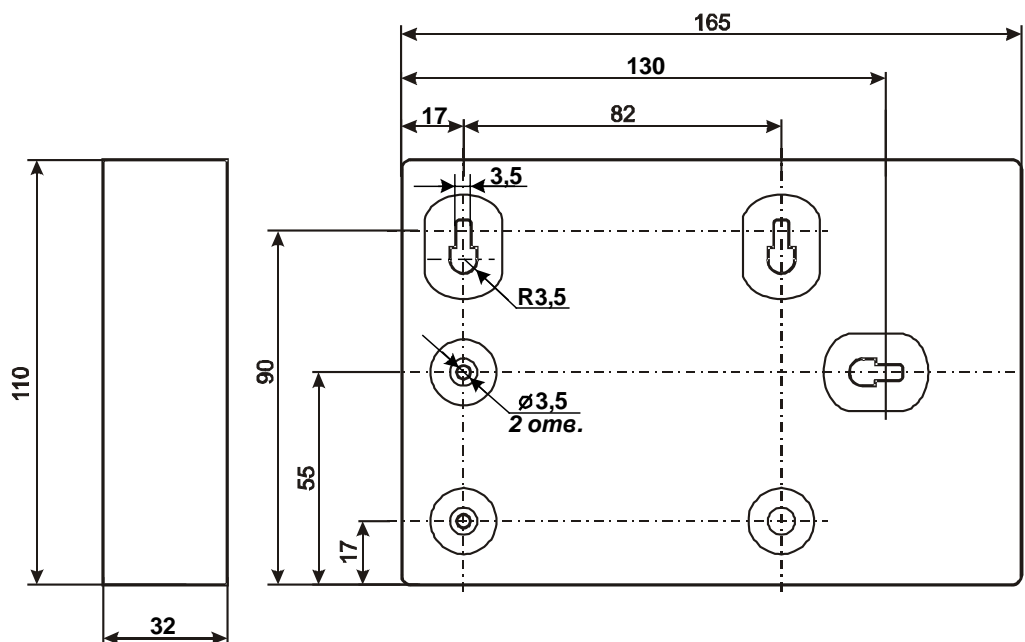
Габаритные и присоединительные размеры КА2, базовый вариант, исп. IP20
